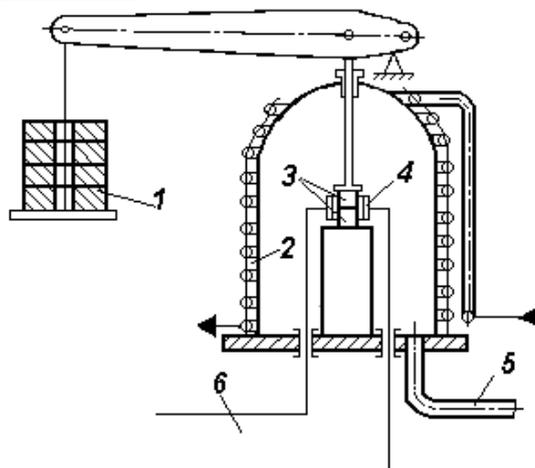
Схема диффузионной сварки в вакууме
